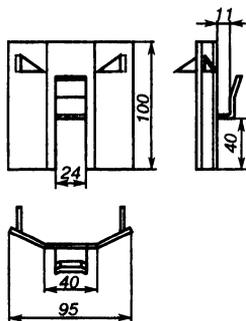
Скоба SH 187 для верхней части оттяжки
